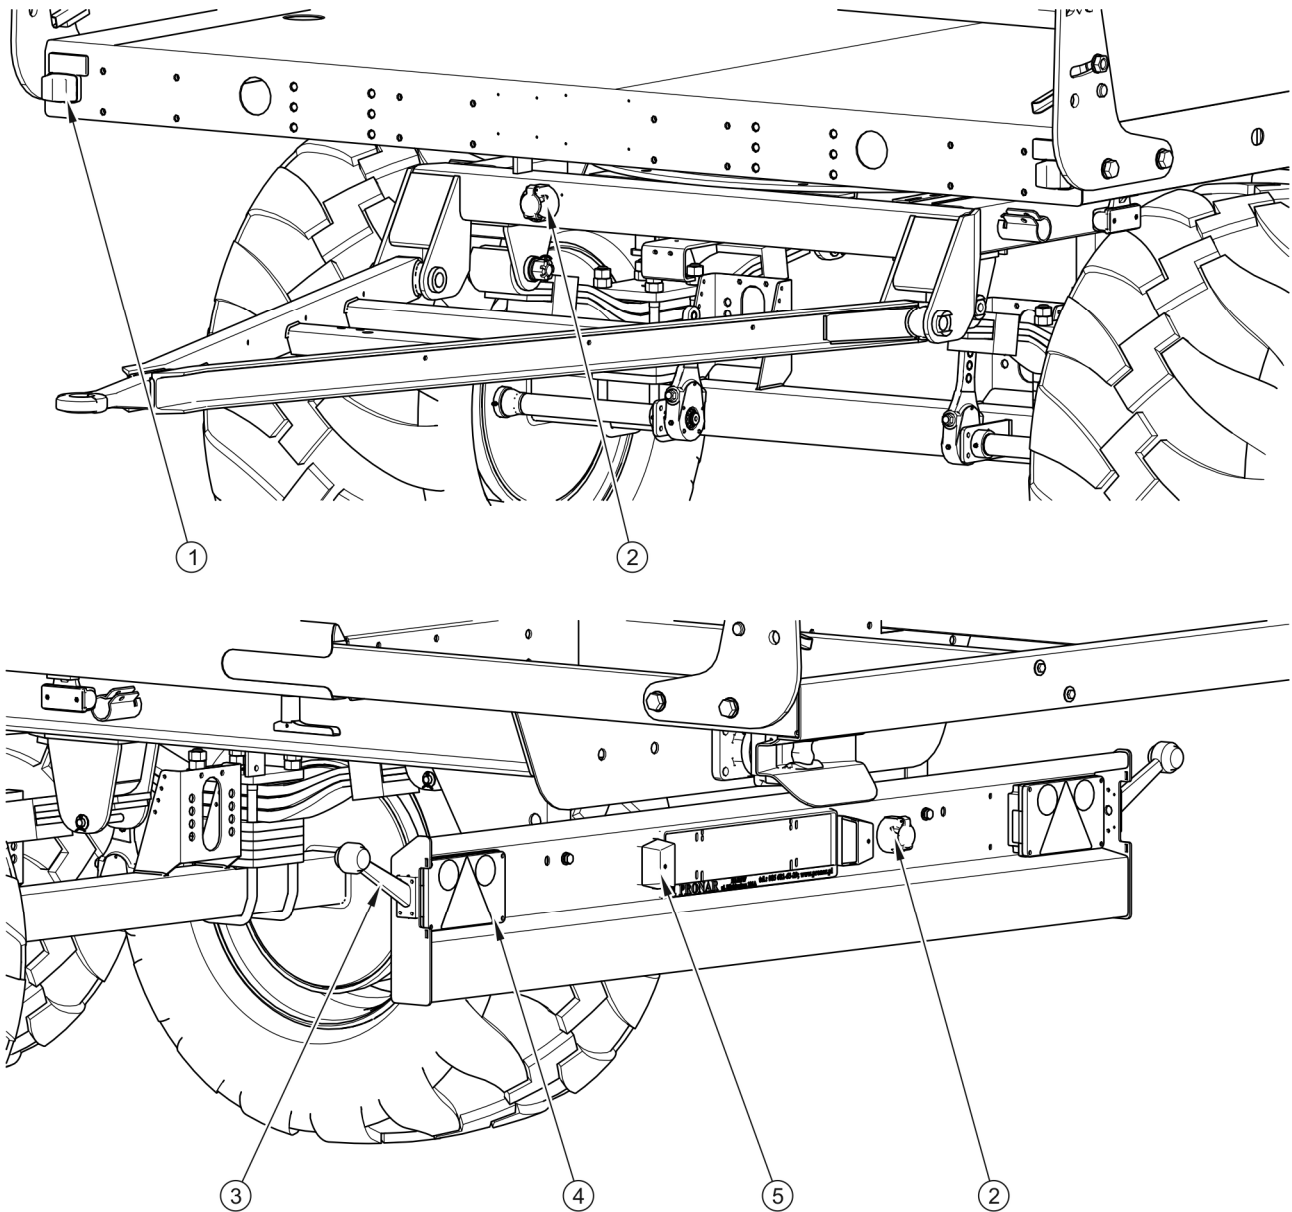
Disposizione degli elementi dell'impianto elettrico
